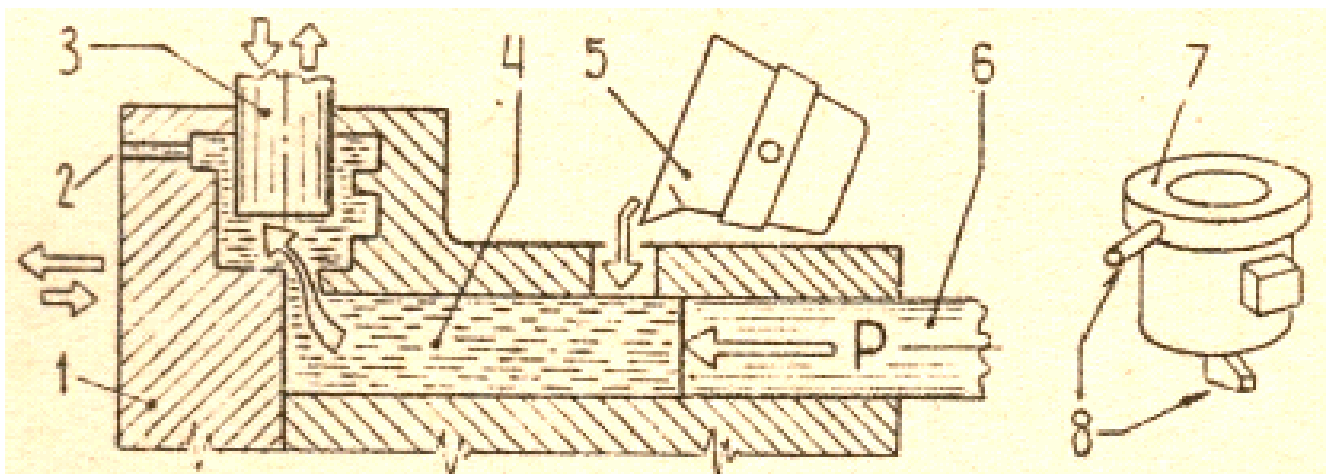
Литье под давлением: 1 — подвижная часть пресс-формы; 2 — выпор; 3 — металлический стержень; 4 — камера сжатия; 5 — заливочный ковш; 6 — поршень, создающий давление; 7 — отливка; 8 — литники
